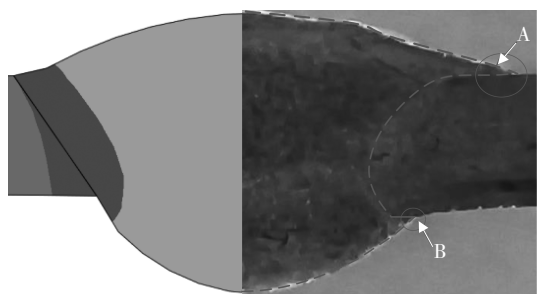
组合热源焊缝截面(左)与实验焊缝(右)
